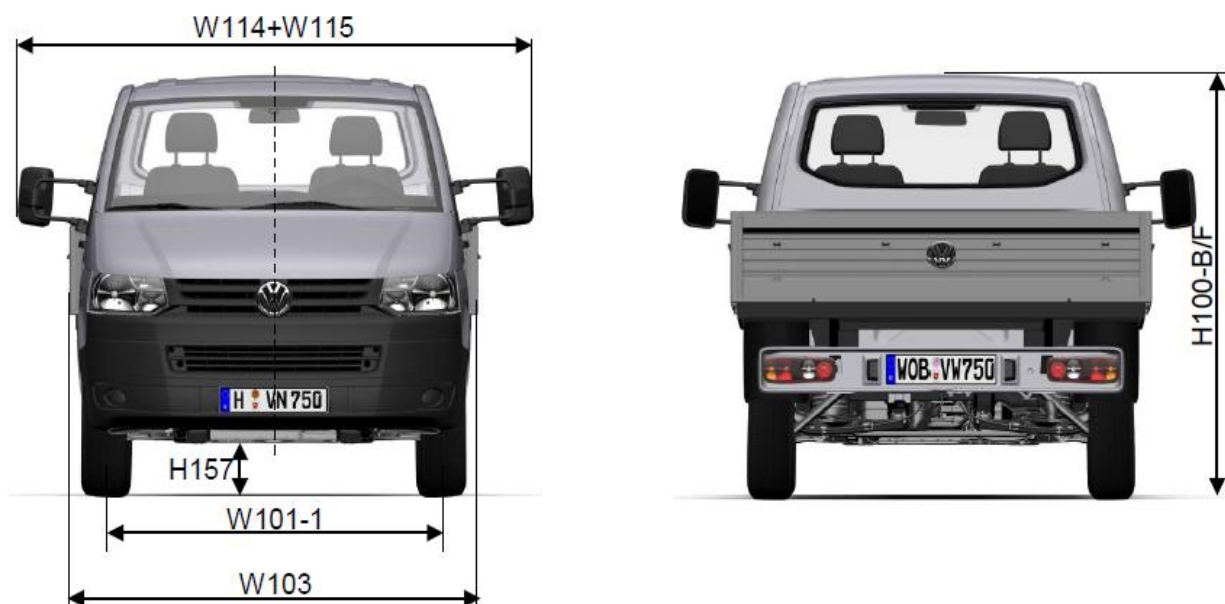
Габариты а/м с бортовой платформой, короткая и длинная база
